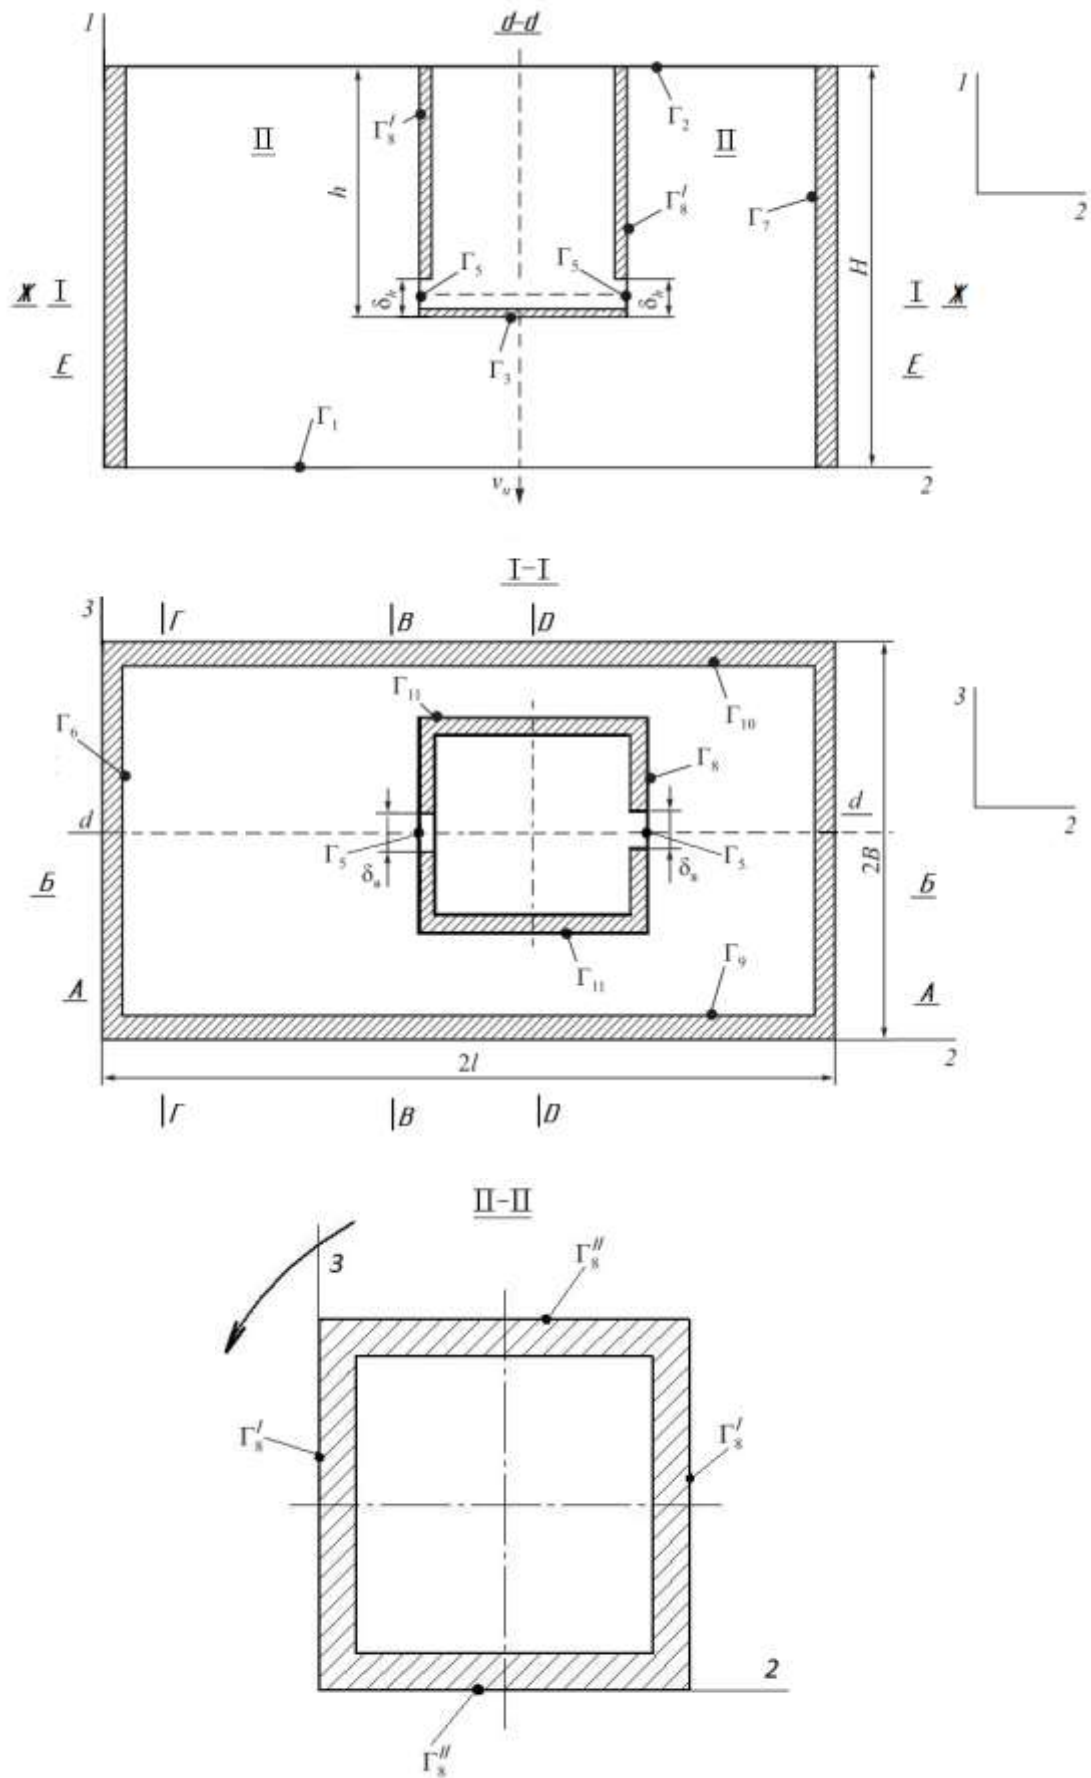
Расчётная схема процесса разливки металла в кристаллизатор
